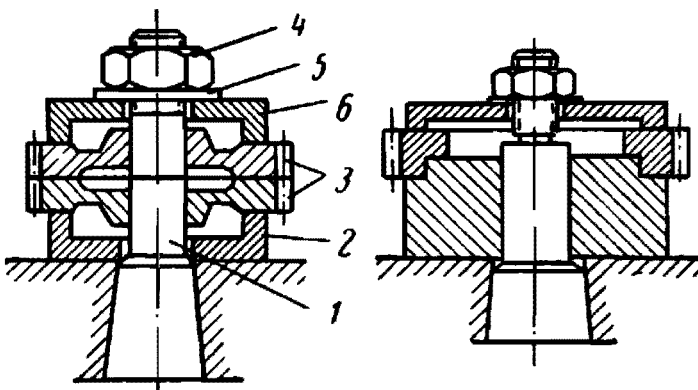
Примеры установки и крепления заготовок нарезаемых зубчатых колес
